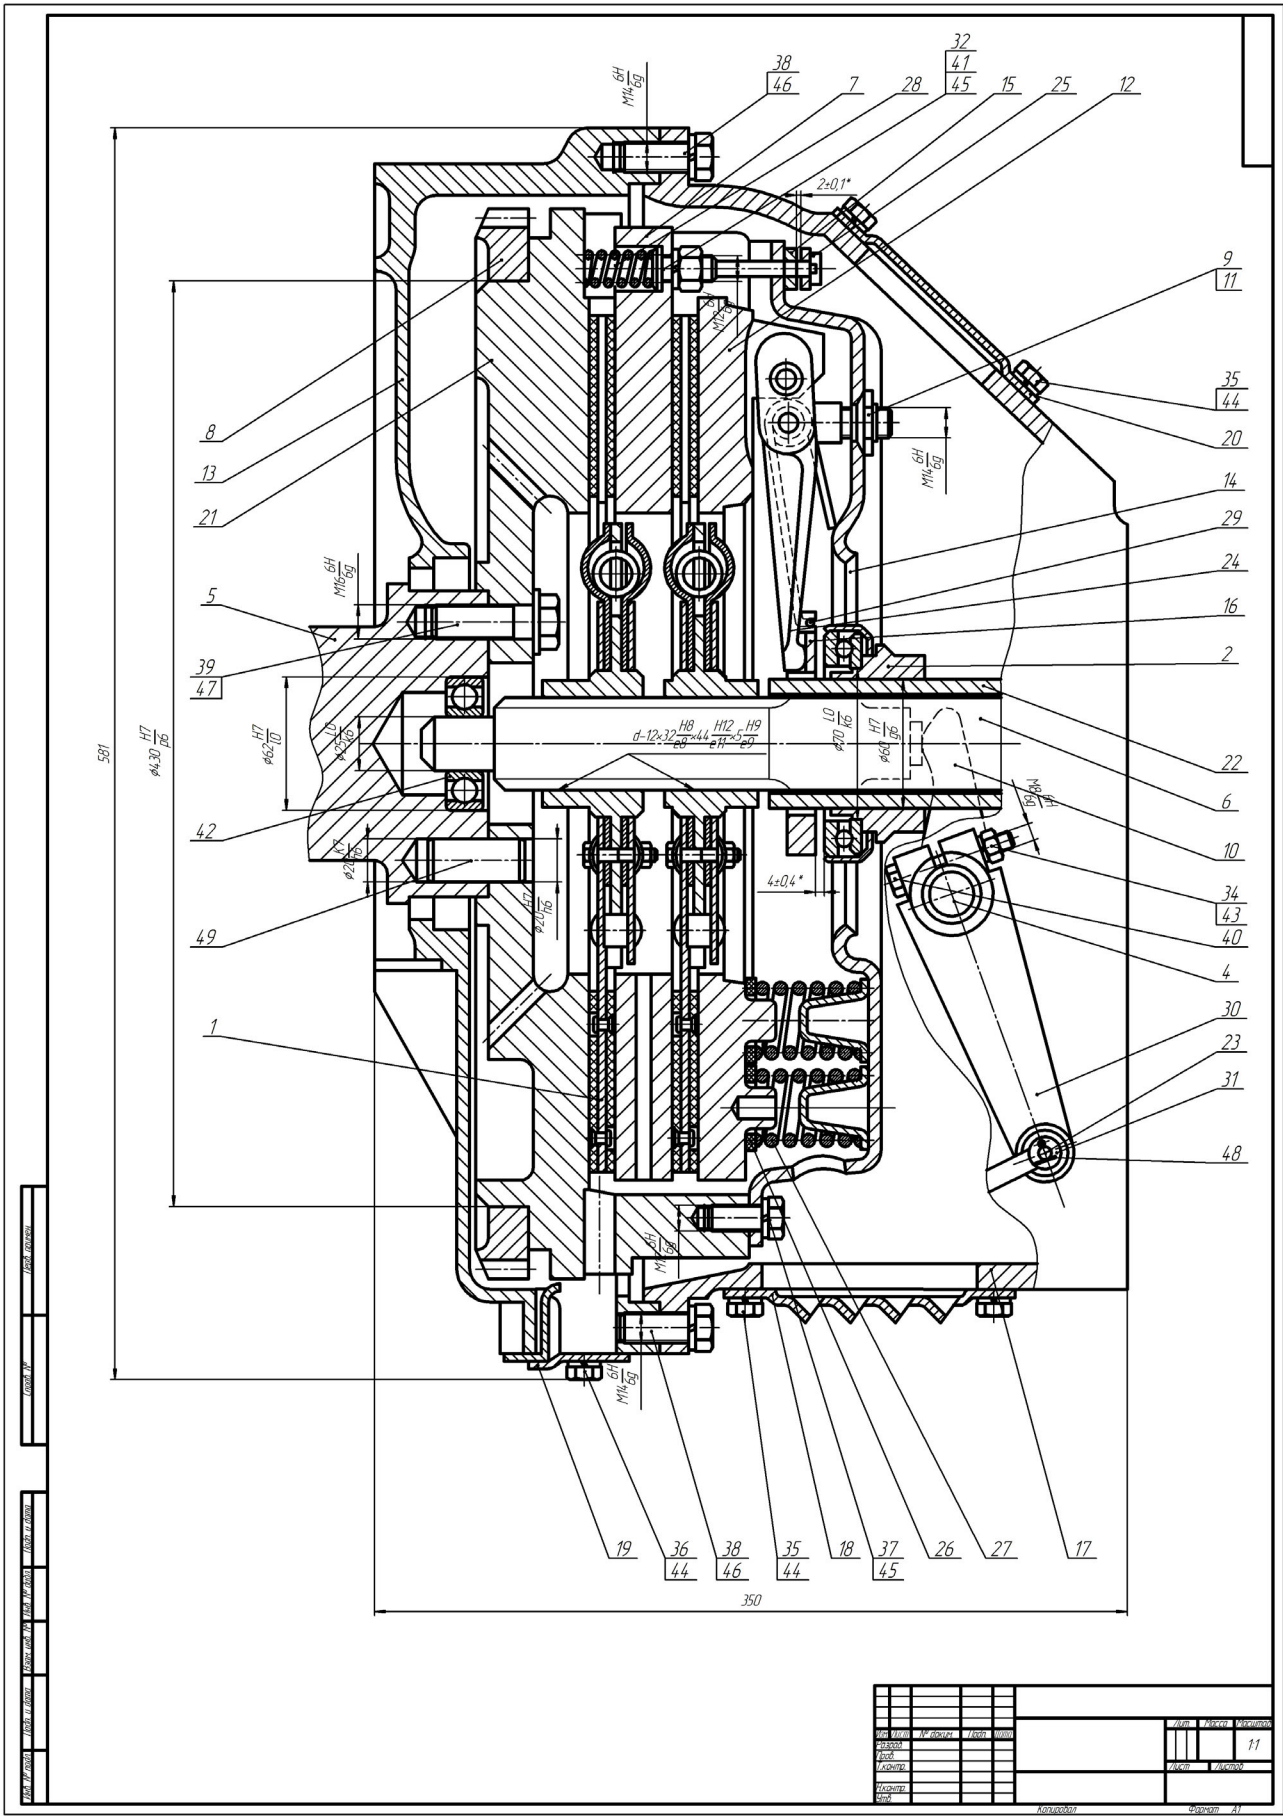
Пример выполнения сборочного чертежа сцепления
